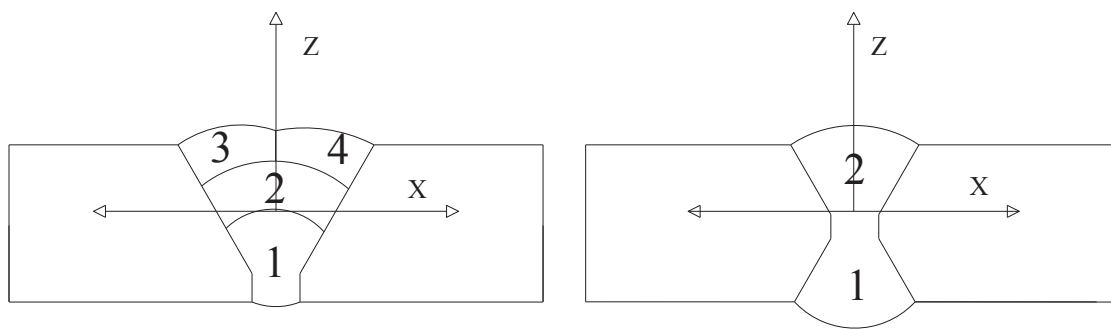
Representación esquemática de la deposición de los cordones de soldadura en las placas soldadas.
